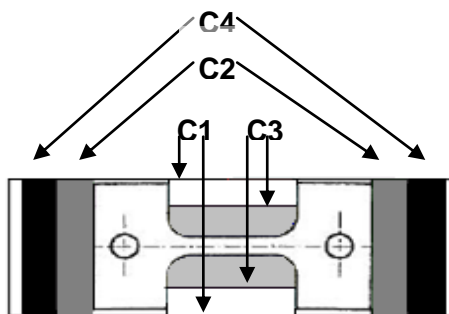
Repères éprouvettes usinées sur chaque plaquette.
